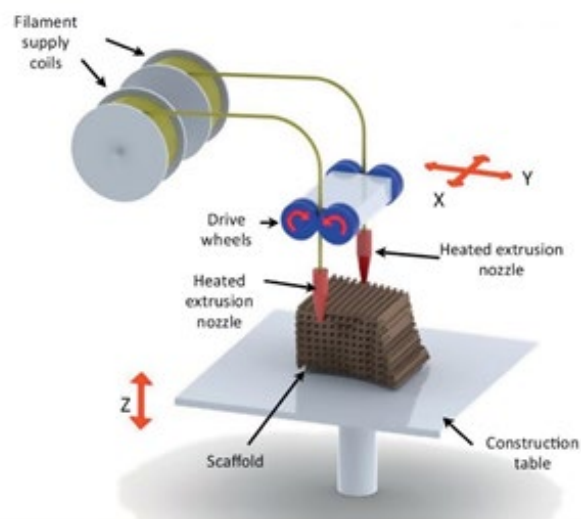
Schéma illustrant l'impression 3D par dépôt de fil fondu (FDM)
